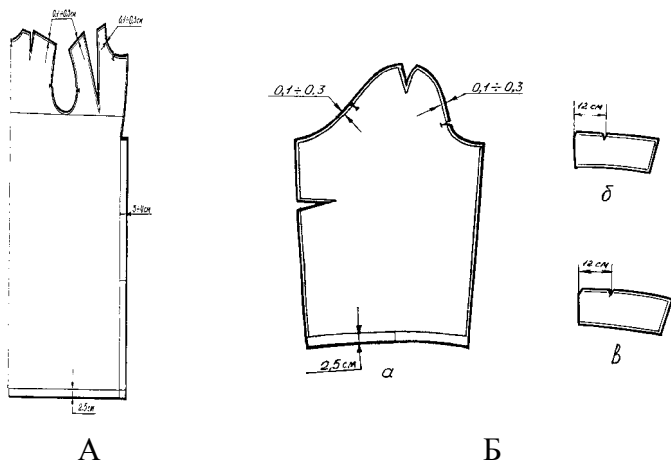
Чертеж лекал деталей мехового изделия, рис. С.В. Гончаровой
